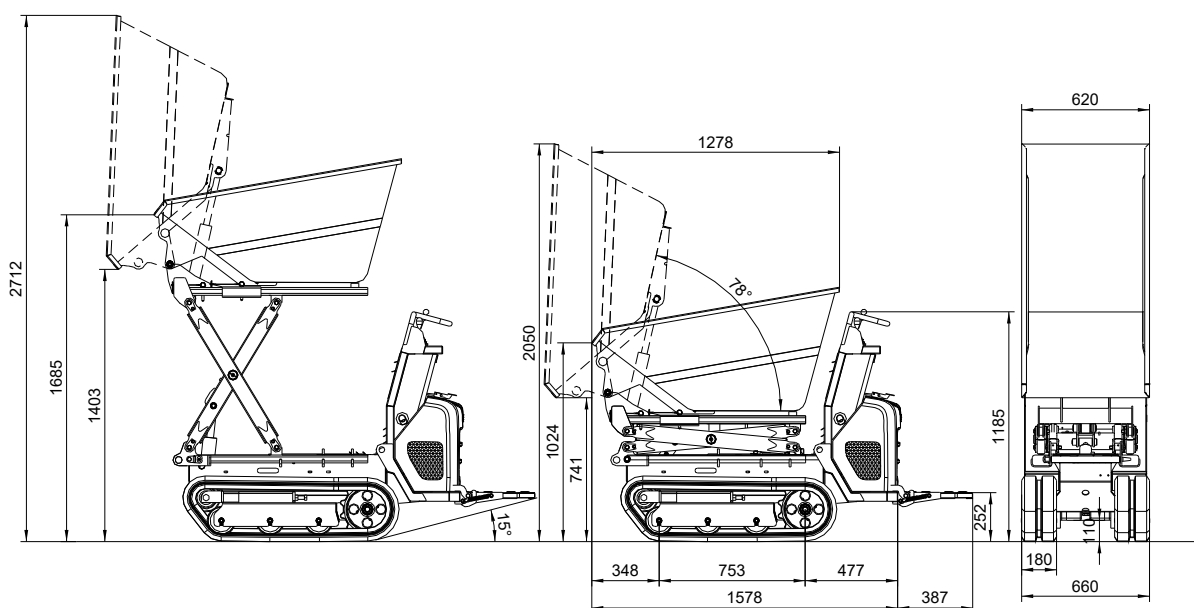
Køretøjets dimensioner (type DT05-P med løftbart tippelad)
